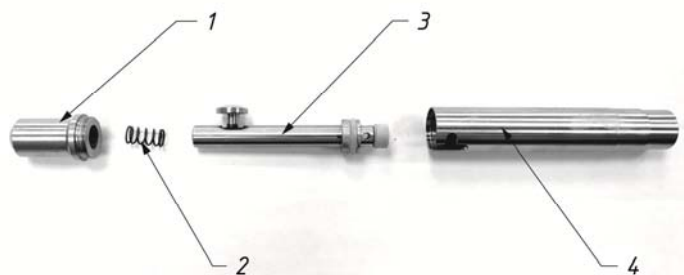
Рукоятка вакуумная, внутренние части
